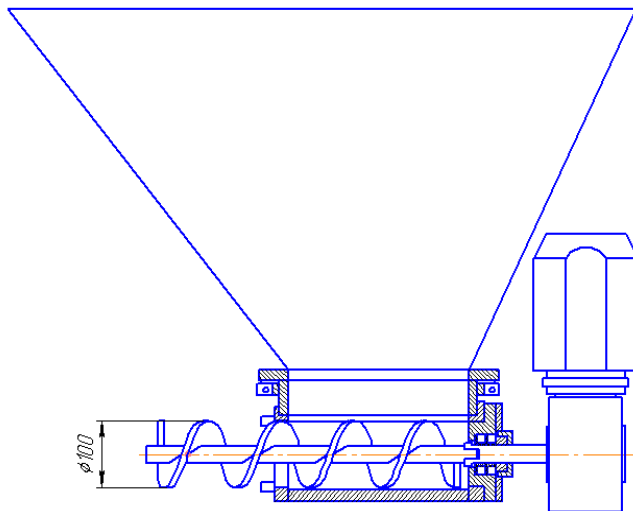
Розрахункова схема живильника: 1-корпус; 2- шнек;
